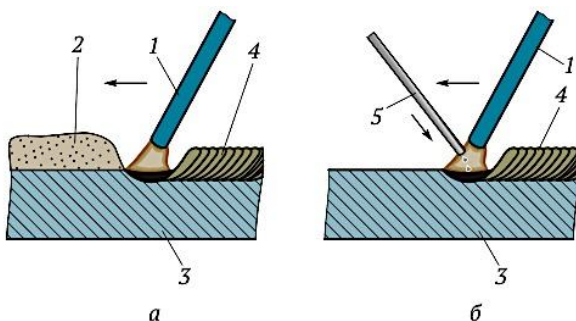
Схема ручной дуговой наплавки неплавящимся электродом:
